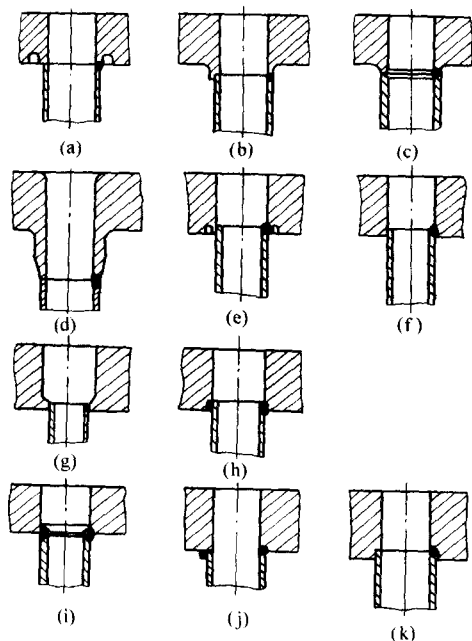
管子与管板内孔焊接的各种接头形式
